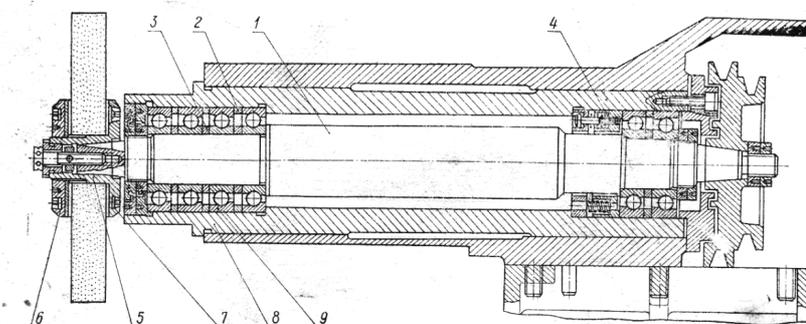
Вид шпиндельного узла бесцентрово-шлифовального станка; 1 - шпиндель, 2, 3 - регулирующие зазор шайбы; 4 - гильза (стакан с термоэлементом); 5 - зажимное крепежное приспособление; 6 - левая шайба; 7 - правая шайба; 8 - корпус шпинделя; 9 - шарикоподшипники передней опоры
